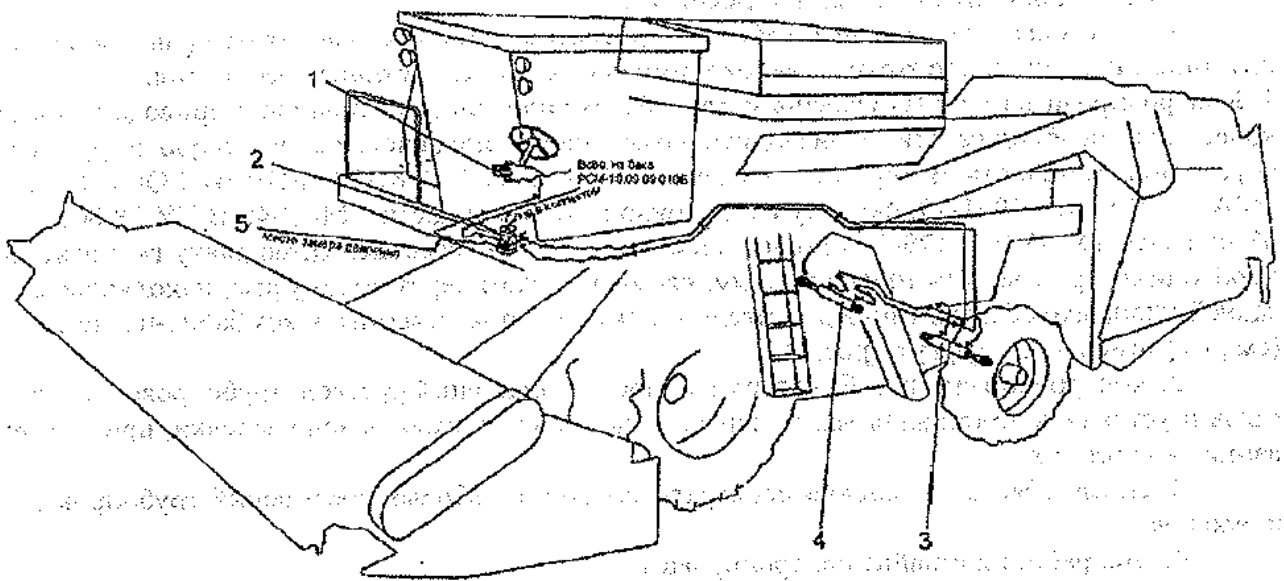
Схема гидросистемы рулевого управления: 1-насос НШ-ЮВ-3-Л (двигатель СМД и Д461-51) или НШ-10Г-3-Л (двигатели ЯМЗ и КАМАЗ); 2-агрегат рулевой АР-125-16; 3, 4- гидроцилиндры управляемых колес ГЦ 50.200.16.000А-01; 5-муфта Н036.67. ЮО-10
